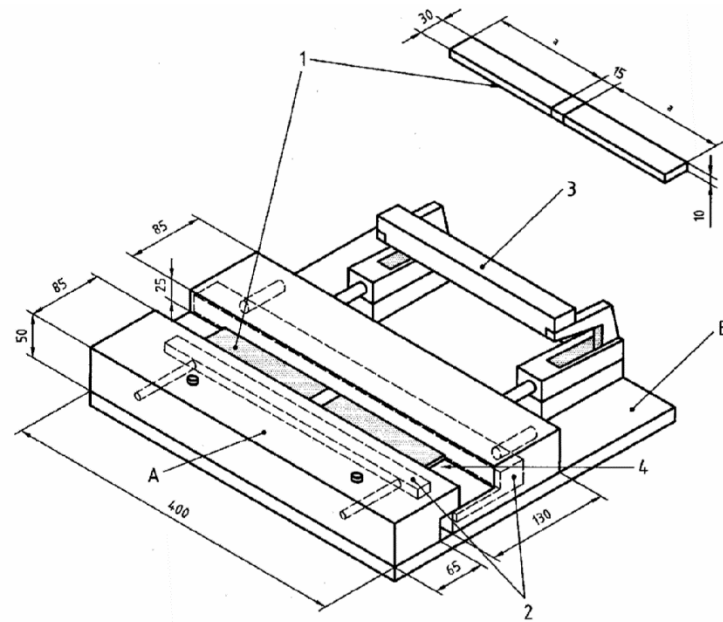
Moldes de Cobre aplicable a heat inputs hasta 2kJ/mm. Diseñado y fabricado en ITMA.
